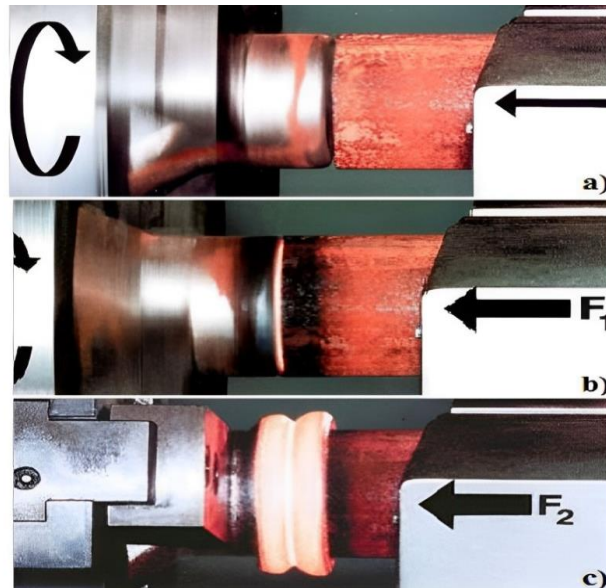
Principe du soudage par friction rotative [24].
